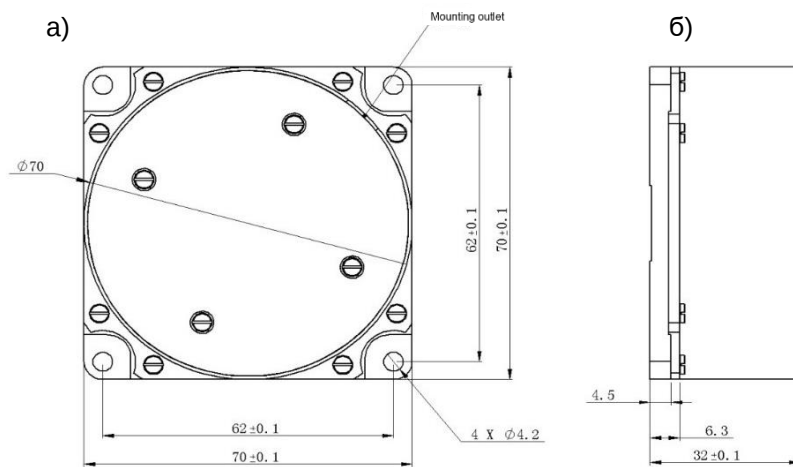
Все размеры в мм а) вид сверху; б) вид сбоку
